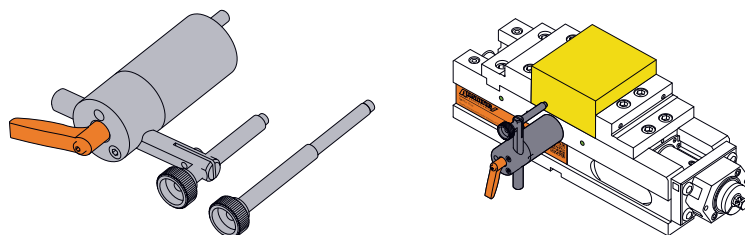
Упор обрабатываемой детали 692 128 5650 144
